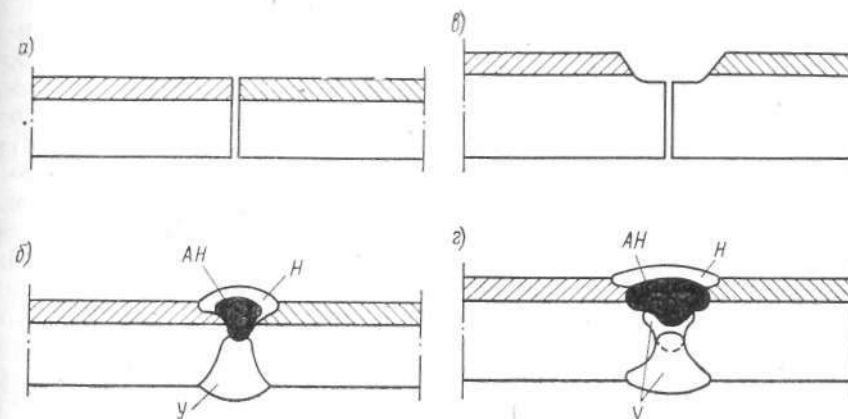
Стыковые соединения двухслойных сталей, выполняемые автоматической сваркой под флюсом: а — вид бескосого соединения; б — схема расположения валиков на бескосом соединении; в — вид соединения со снятым плакирующим слоем; г — схема расположения валиков на соединении со снятым плакирующим слоем.
